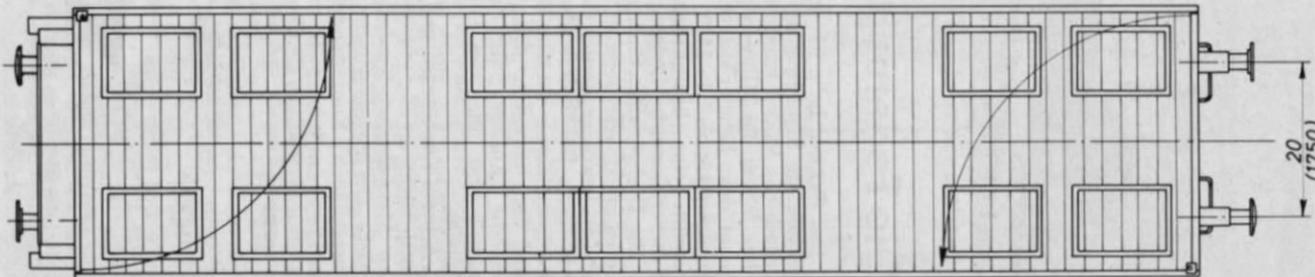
und 4. Seitenansicht und Draufsicht des OOfs-47 im Zeichnungsmaßstab 1 : 87. In Klammern = Originalmaße in mm.
